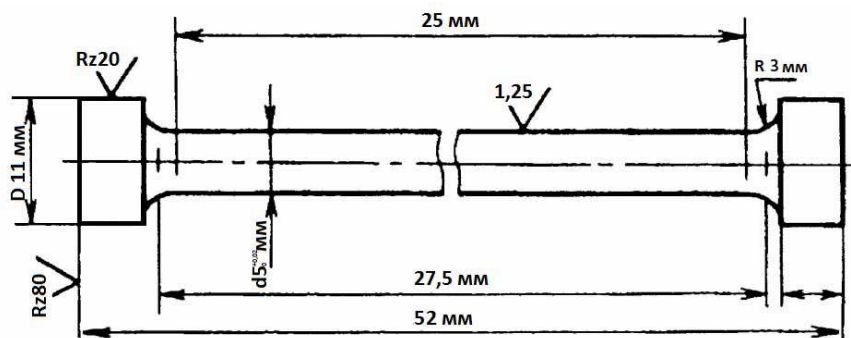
Чертеж образца для механических испытаний на растяжение
